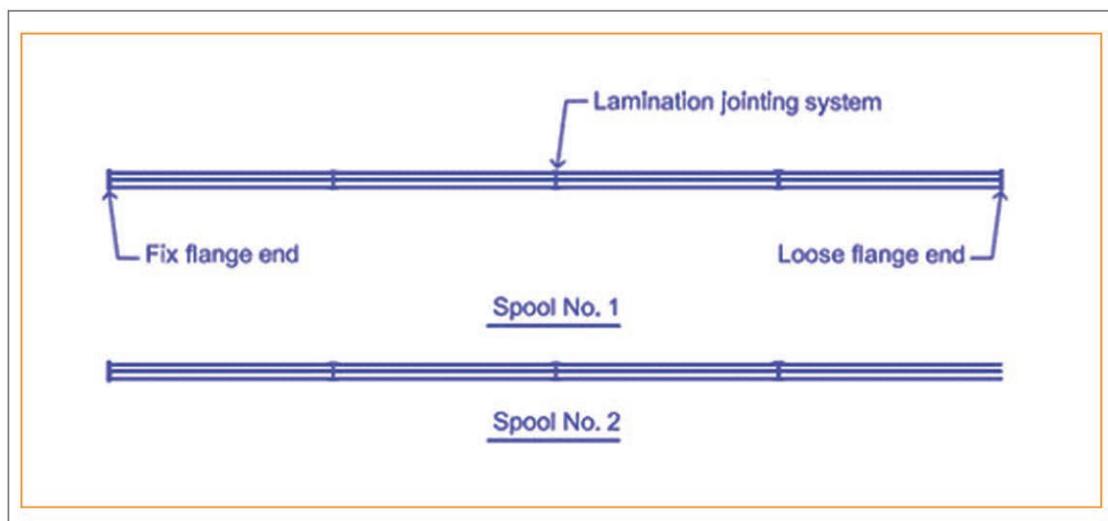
Изготовление трубных секций со сварными соединениями
